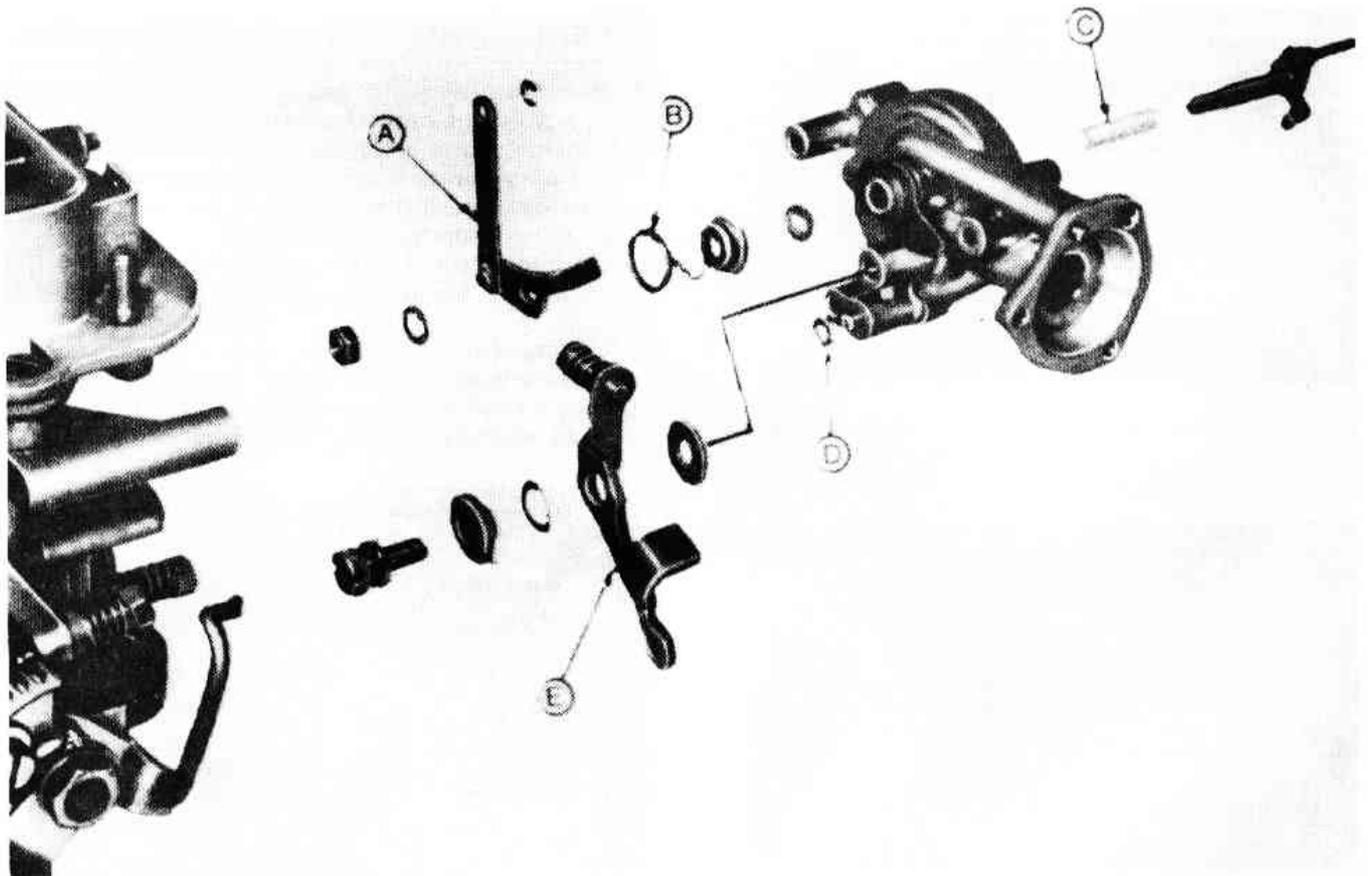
Детали автоматической заслонки карбюратора "Вебер" (Разд. 27)
